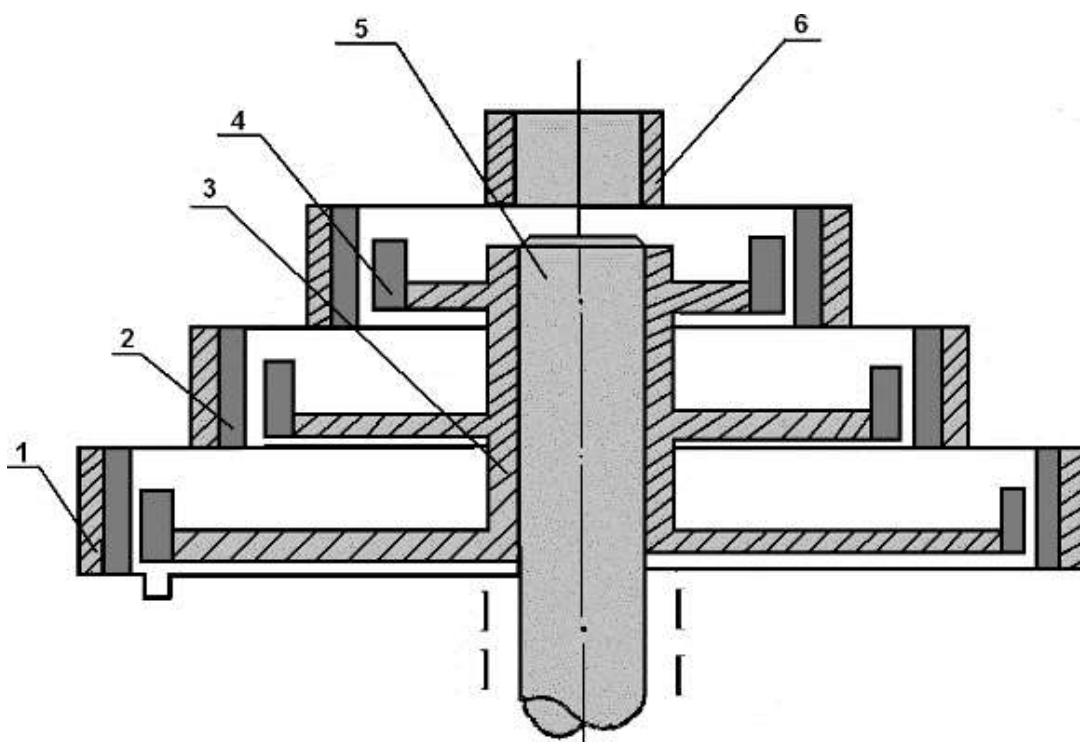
Трехступенчатый узел измельчения: 1 – Многоступенчатый корпус; 2 – Отражательные плиты; 3 – Ступенчатый ротор; 4 – Било; 5 – Вал; 6 – Загрузочный патрубок
